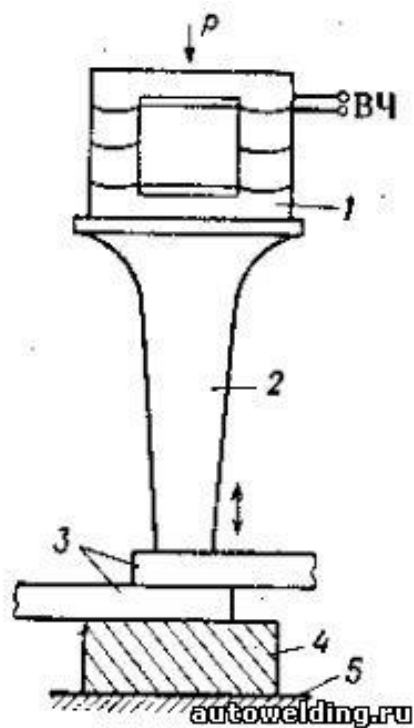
Схема сварки пластмасс ультразвуком: 1 — вибратор; 2 — концентратор; 3 — свариваемый материал; 4 — отражатель; 5 — опора
